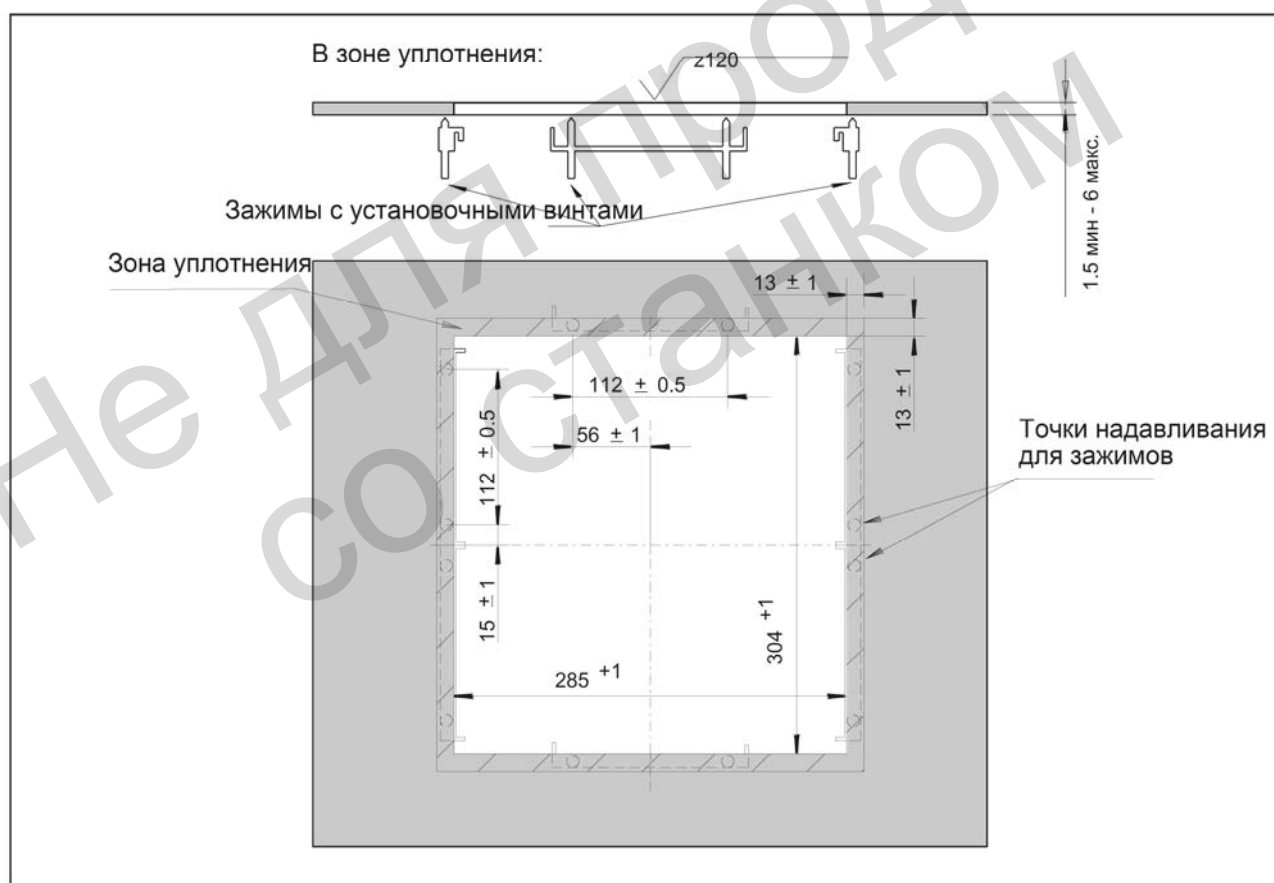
Габаритный чертеж для монтажа панели оператора OP 010S
